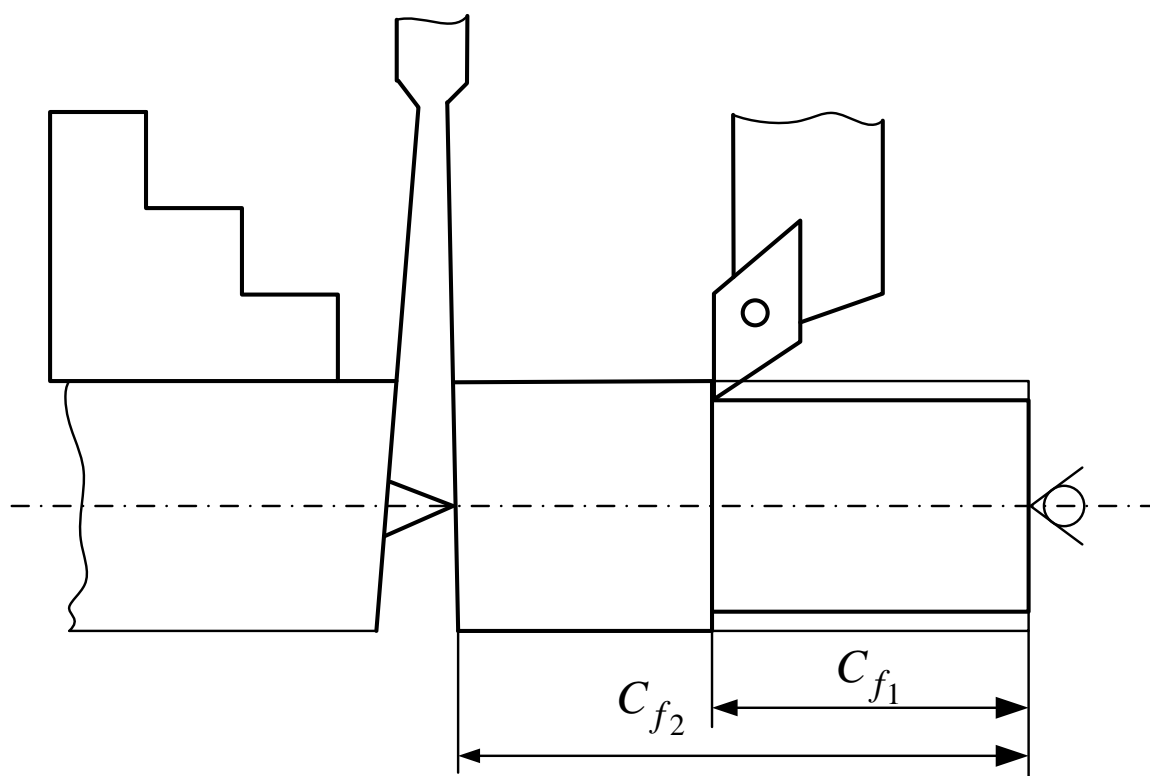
Схема обработки детали на станке-полуавтомате
